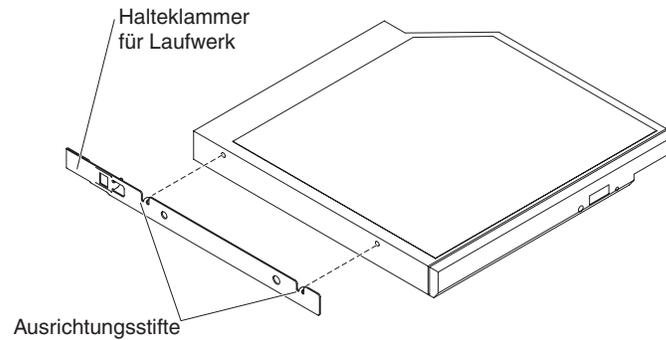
Halteklammer des DVD-Laufwerks entfernen
